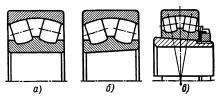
Роликоподшипники радиальные двухрядные самоустанавливающиеся: а—с цилиндрическим отверстием, тип 3000, ГОСТ 5721—57; б—с коническим отверстием (конусность 1/12), тип 113000, ГОСТ 5721—57; в—на закрепительной втулке, тип 13000, ГОСТ 8545—57
